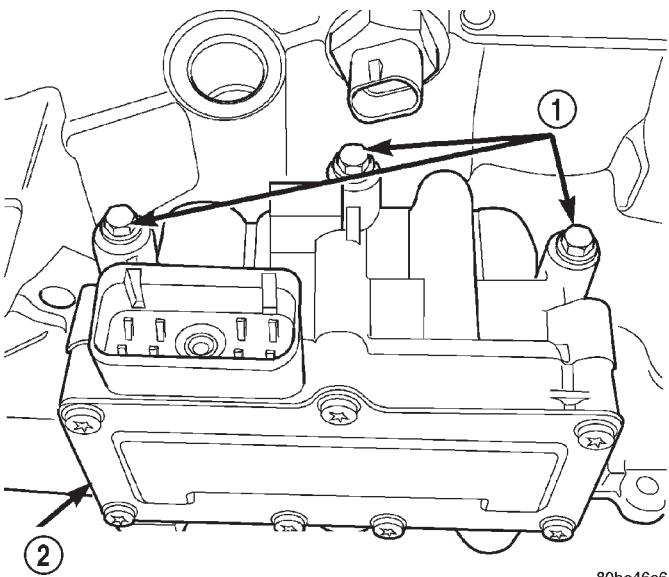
Pernos del conjunto de solenoides y conmutadores de presión al cárter
